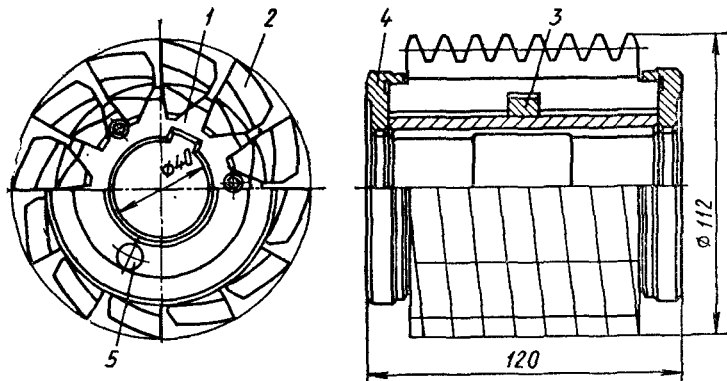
Сборная незатылованная червячная фреза с поворотными рейками
